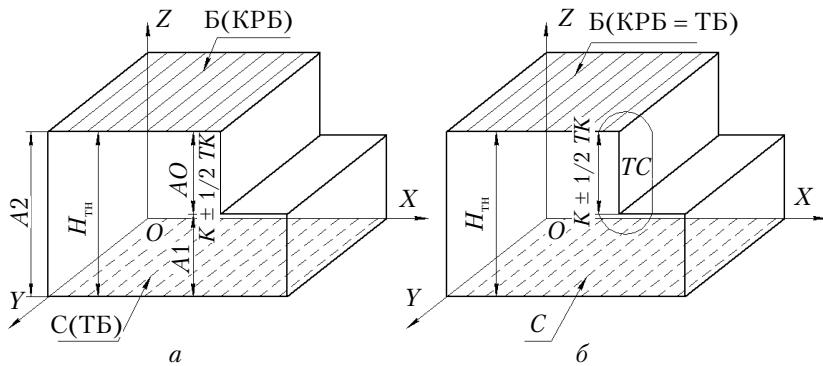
Два варианта базирования заготовки при фрезеровании уступа на детали (a — принцип совмещения баз не выполняется; b — принцип совмещения баз выполняется)
